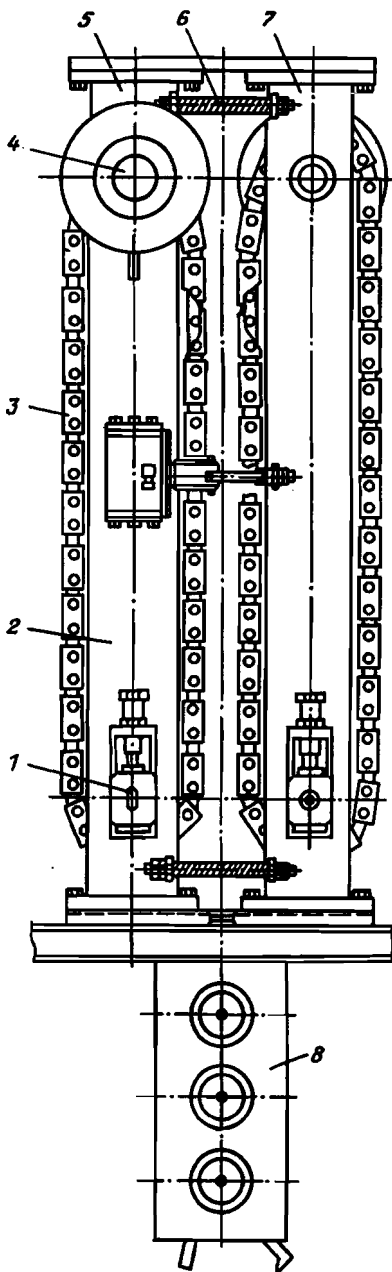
Схема транспортера с двумя цепями и механическим регулированием прижима плашек и натяжения цепей:
